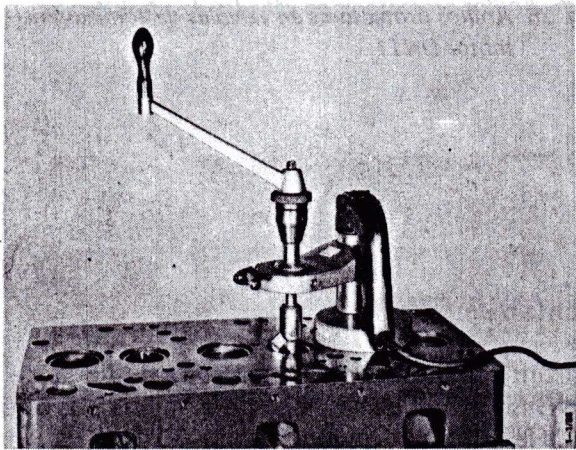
Ejemplo de herramienta para el repasado del asiento de válvula
